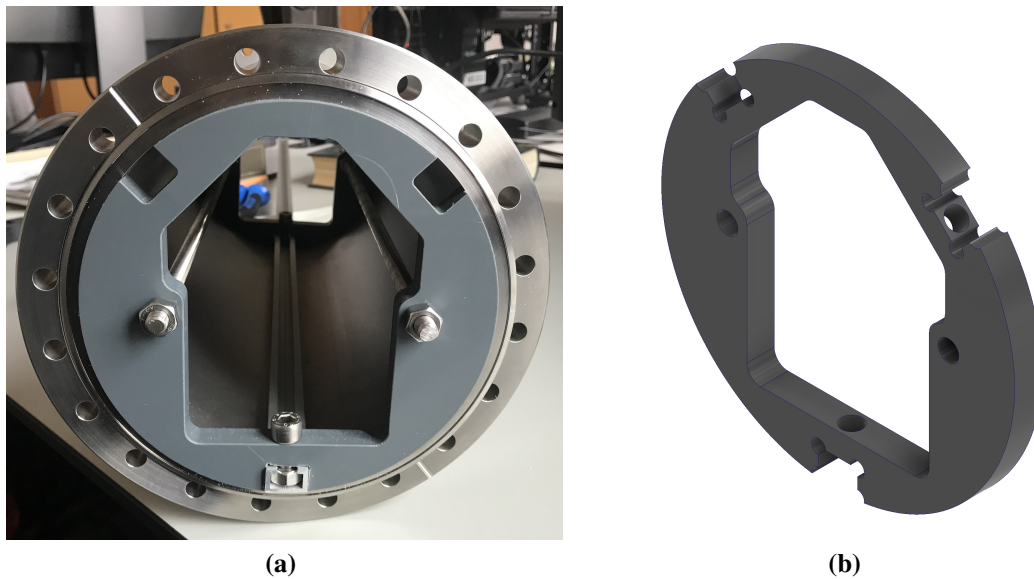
Einsatz, welcher in den Flansch eines Strahlrohrs gesteckt wird. Durch die Gewindestangen werden die zwei gegenüberliegenden Platten an die Schweißnaht zwischen Flansch und Rohrstück gepresst.
